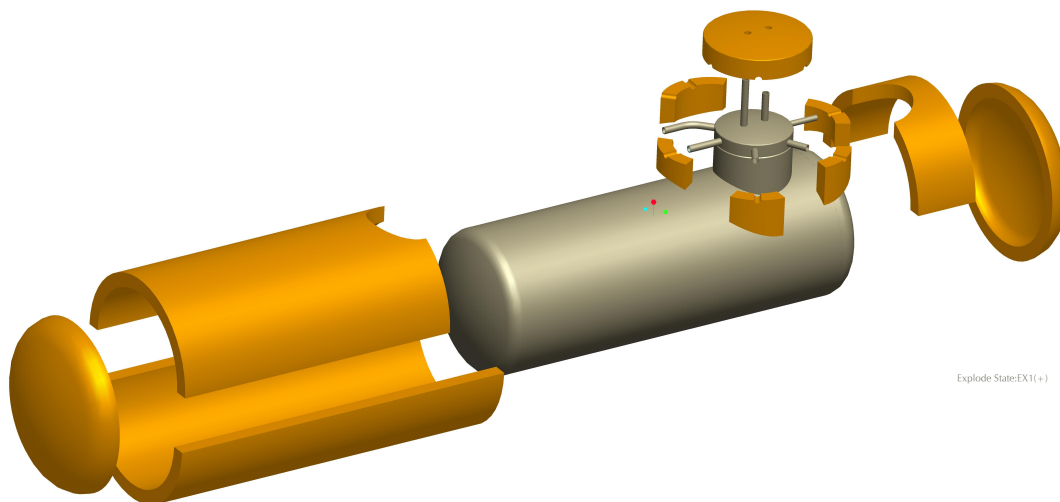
Explosionszeichnung des Aluminiumtanks und der Komponenten der Tankisolation
